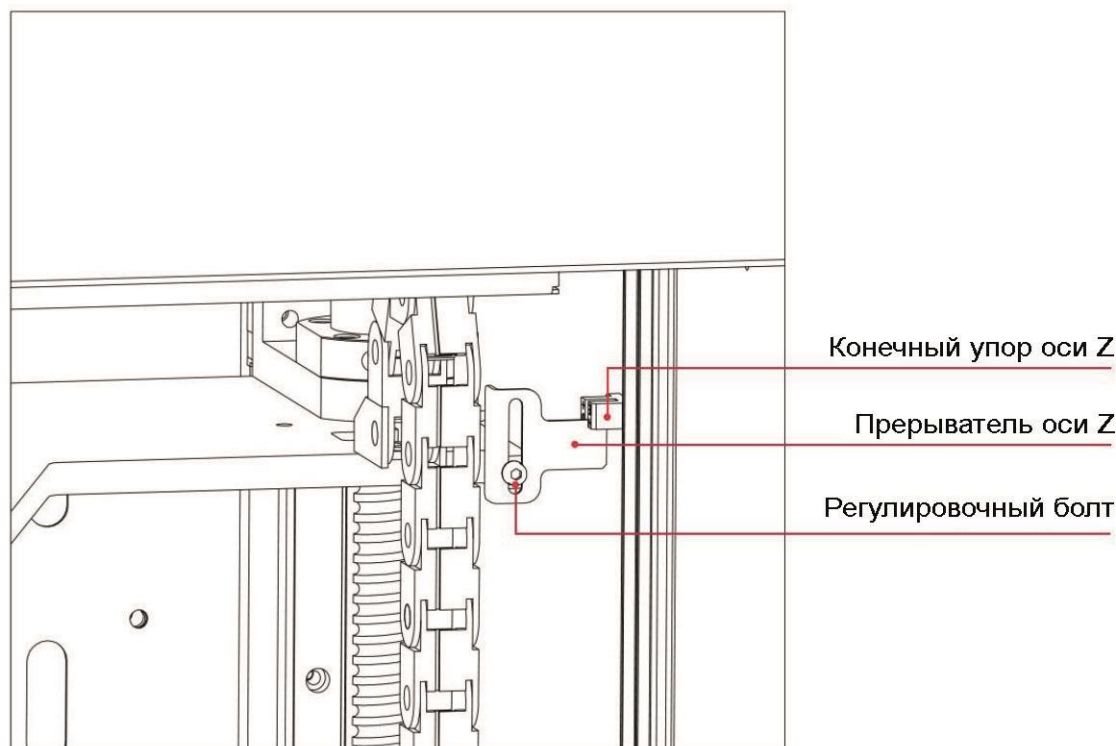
Концевой упор и концевой прерыватель, расположенные с правой стороны нагревательного стола
